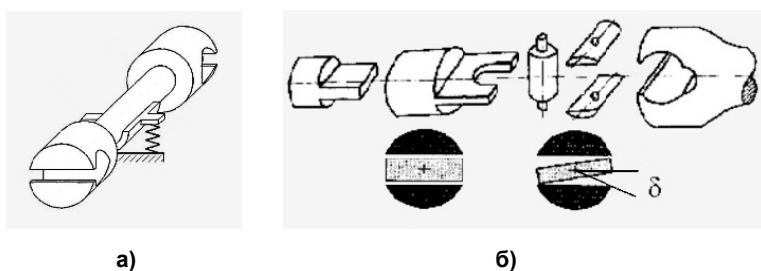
Шпиндель в сборе (а) и конструкция скользящего блока (б):
